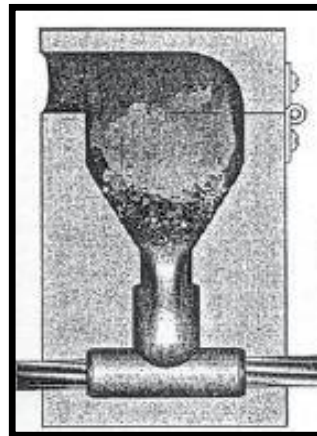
Fin de colada y formación de soldadura.
